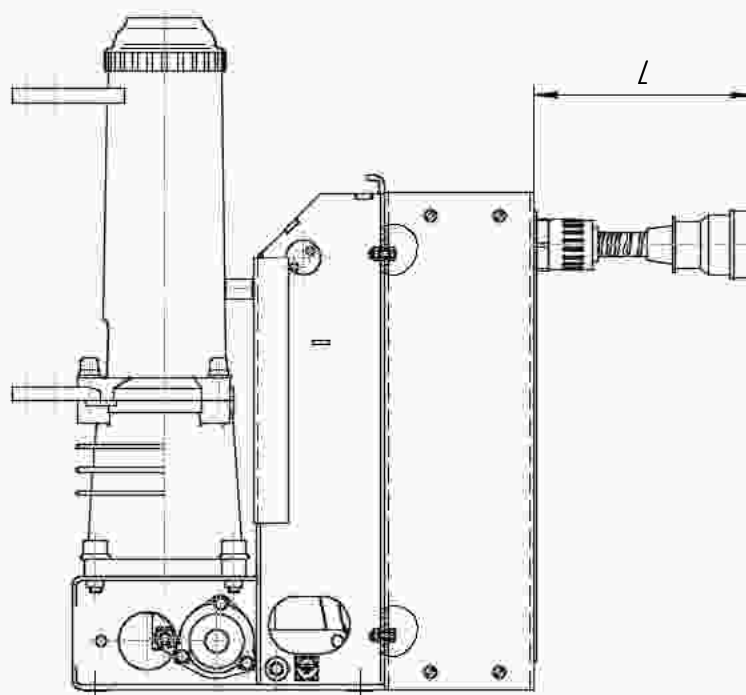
Габаритные, присоединительные и установочные размеры выключателей ВВУ-СЭЩ-ПЗ-10-20(31,5)/ для К-26 (остальное смотреть рисунок Б.1)
